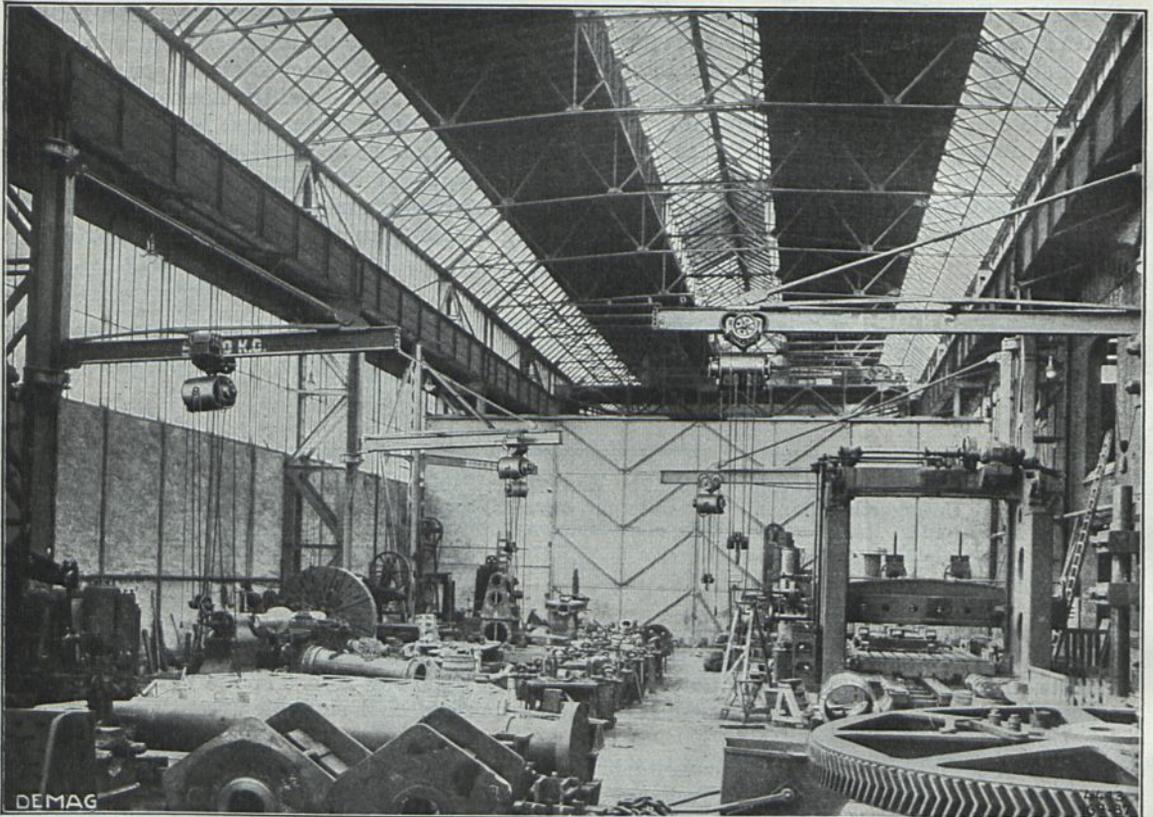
Schwenkkrane mit Eltflaschenzügen in der Bearbeitungswerkstatt einer Werft, Ausführung der Deutschen Maschinenfabrik A. G., Duisburg.
